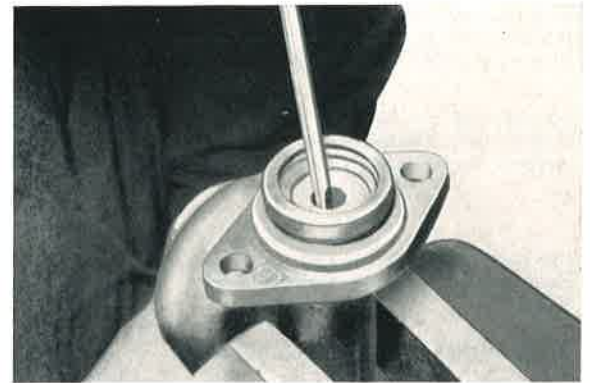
Wenn das Ventil nicht gleich hochkommt, mit Schraubenzieher kurz andrücken und Feder belasten.
